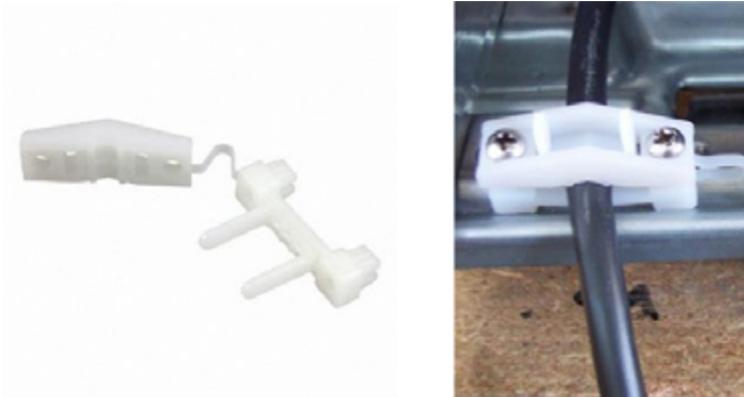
Detailansicht doppelte Kabelbefestigung
